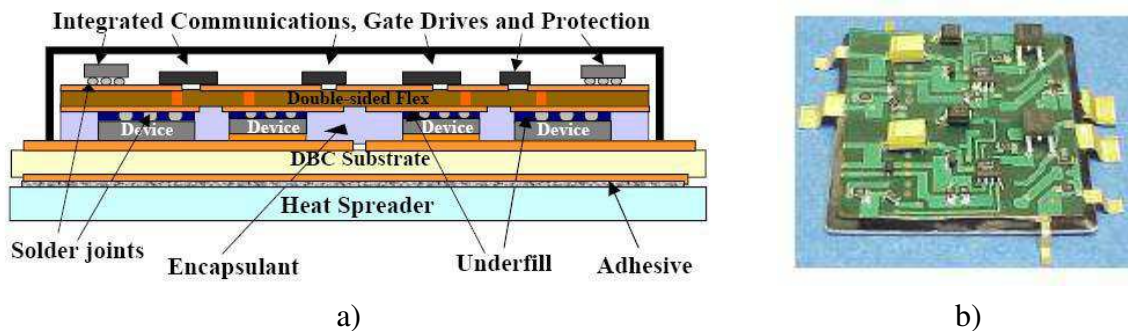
Module de puissance *Flip chip on Flex* utilisant la technologie *solder bump* [26]
